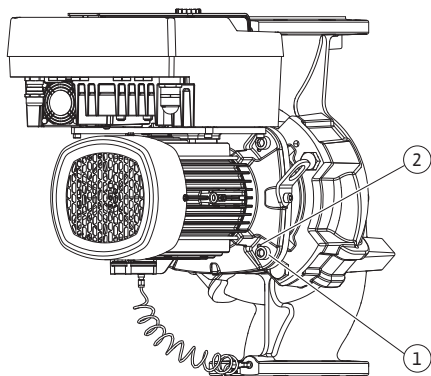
Abdrücken des Einstecksatzes über Gewindebohrungen
